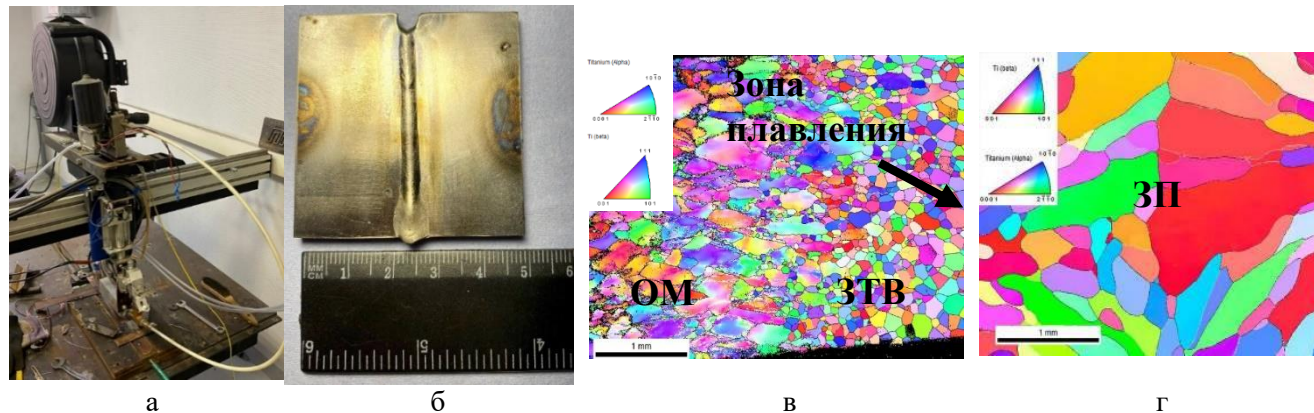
Оборудование для ПС (а) и внешний вид сварного соединения толщиной 4 мм (б), а также EBSD карты сварного соединения из сплава ВТИ-4 в поперечном сечении сварного шва, полученного плазменной сваркой проникающей дугой: от ЗТВ до зоны сплавления (в); центр сварного шва (г)
